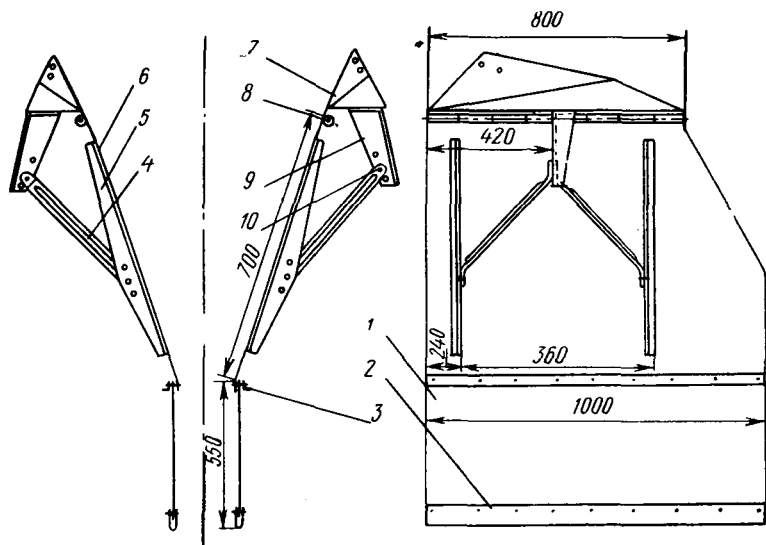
Приспособление ВО-0,8 к копнителю для формирования валков соломы:
